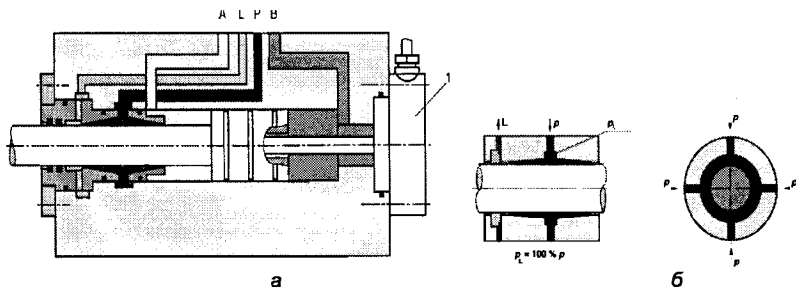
Схеми сервоциліндра з опором штока у вигляді гідростатичного клинового зазору (а) та опори штока (б)
